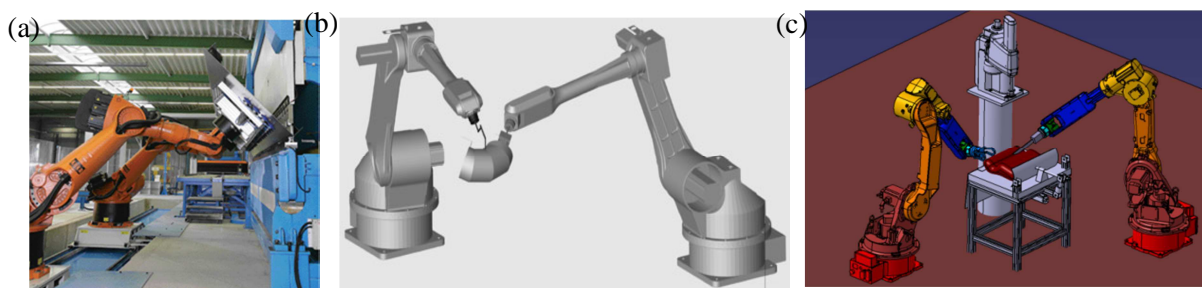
Travail collaboratif de deux robots : manipulation de tôle [Metalforming 2007] (a) soudage [Zhang *et al.* 2012] (b), découpe de corps mous – projet ANR ARMS (c)
